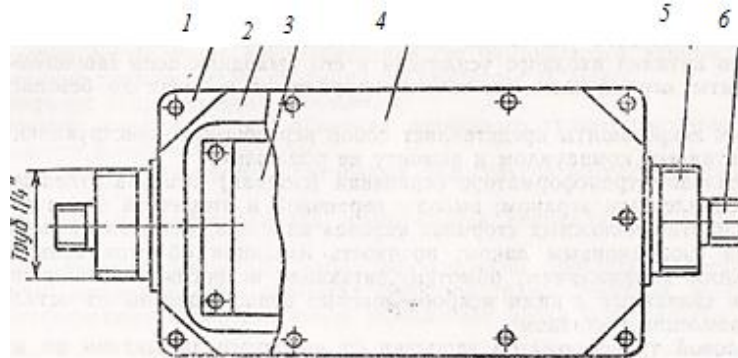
Блок іскрозахисту: 1-корпус, 2-прокладка, 3-плата; 4-кришка; 5-фланець; 6-вилка
